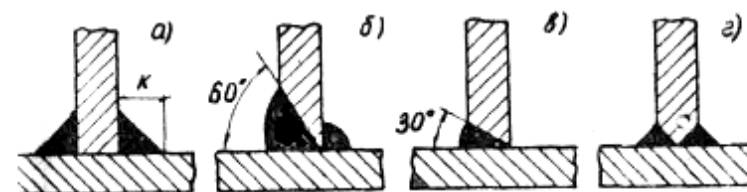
Виды тавровых сварных соединений
